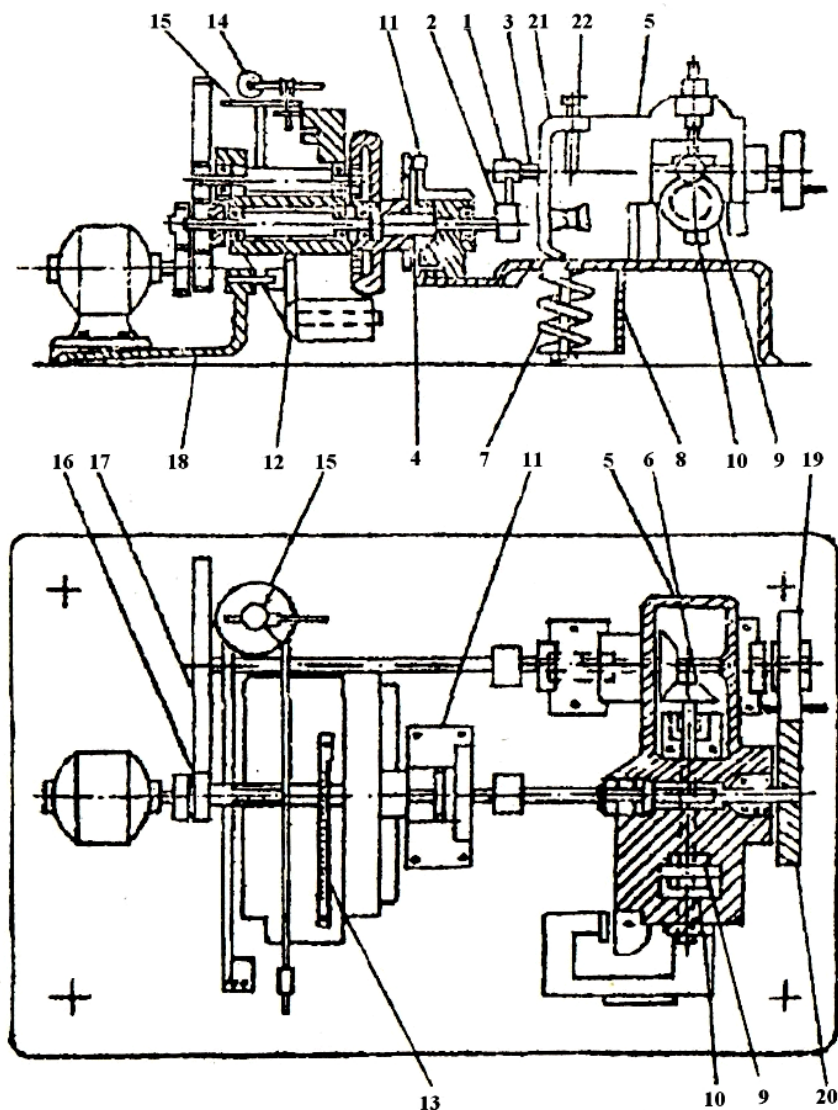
Схема устройства машины МИ-ИМ: 1 - верхний шпиндель; 2 - нижний шпиндель; 3, 4, 6 - валы; 5 - рама; 7 - пружина; 8 - шкала; 9, 10 - обоймы эксцентрика; 11 - счетчик; 12 - силоизмеритель; 13 - линейка; 14 - барабан; 15 - диск; 16, 17, 19, 20 - шестерни; 18 - корпус; 21 - скоба; 22 - винт
